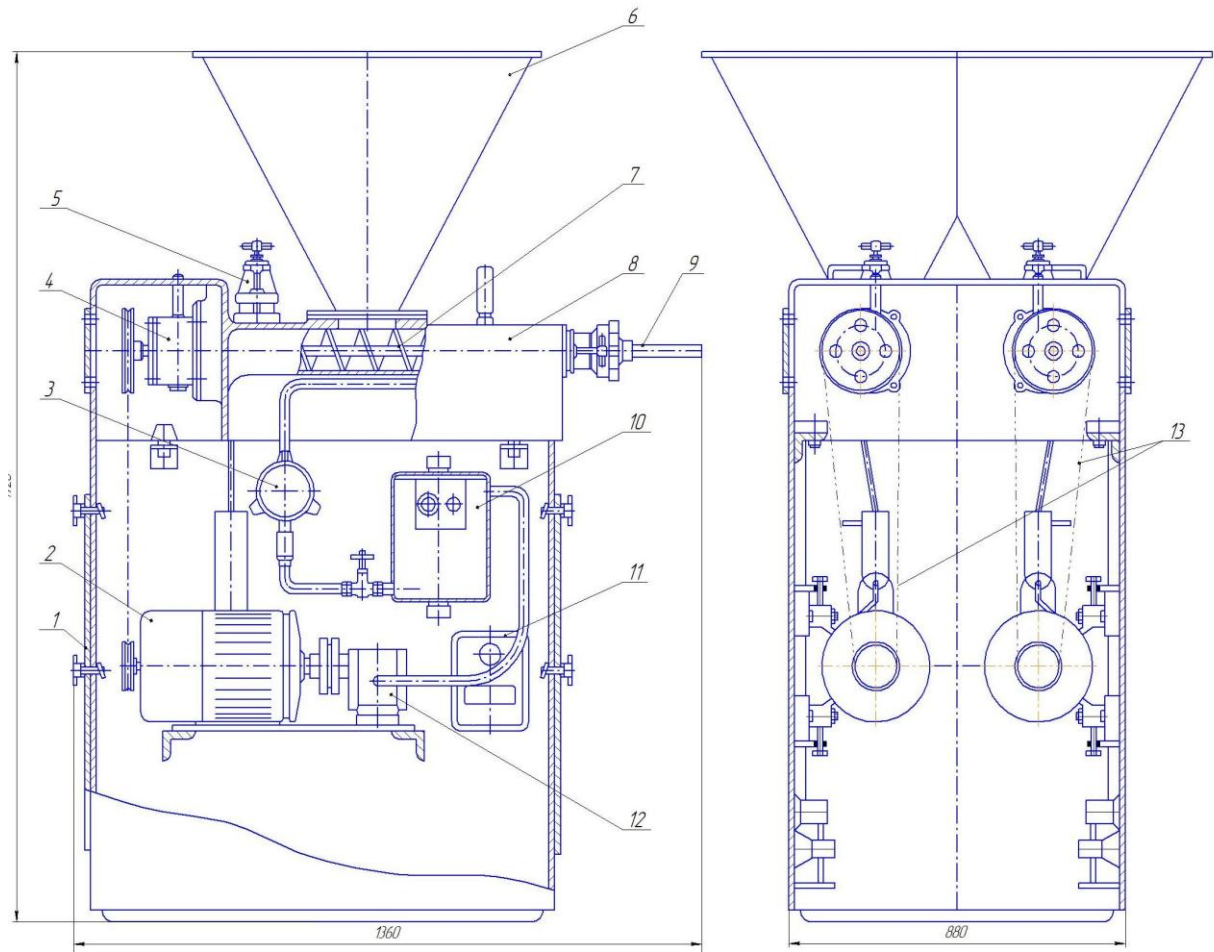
Вакуумный шприц непрерывного действия: 1 - станина; 2 - электродвигатель; 3 - отстойник; 4 – редуктор; 5 – вакуумная головка; 6 - бункер; 7 – шнек; 8 - головка рабочих цилиндров; 9 – цевка; 10- масляный бак; 11 – магнитный пускатель; 12 – масляный насос; 13 – цепная передача
